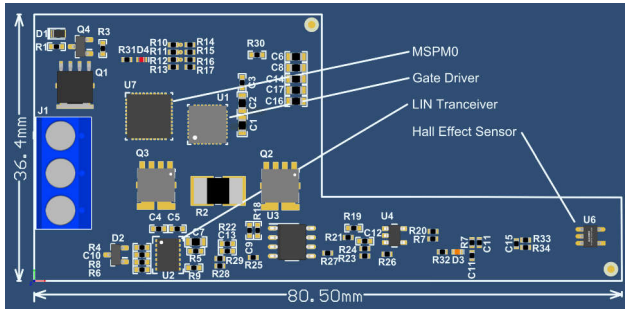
车窗升降用紧凑型 L 形智能执行器 PCB
